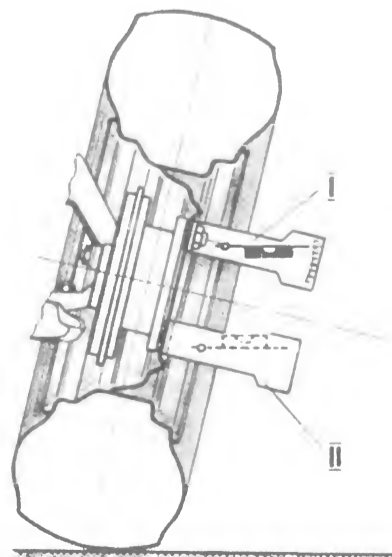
Схема измерения угла развала: I и II — первое и второе положения приспособления.
